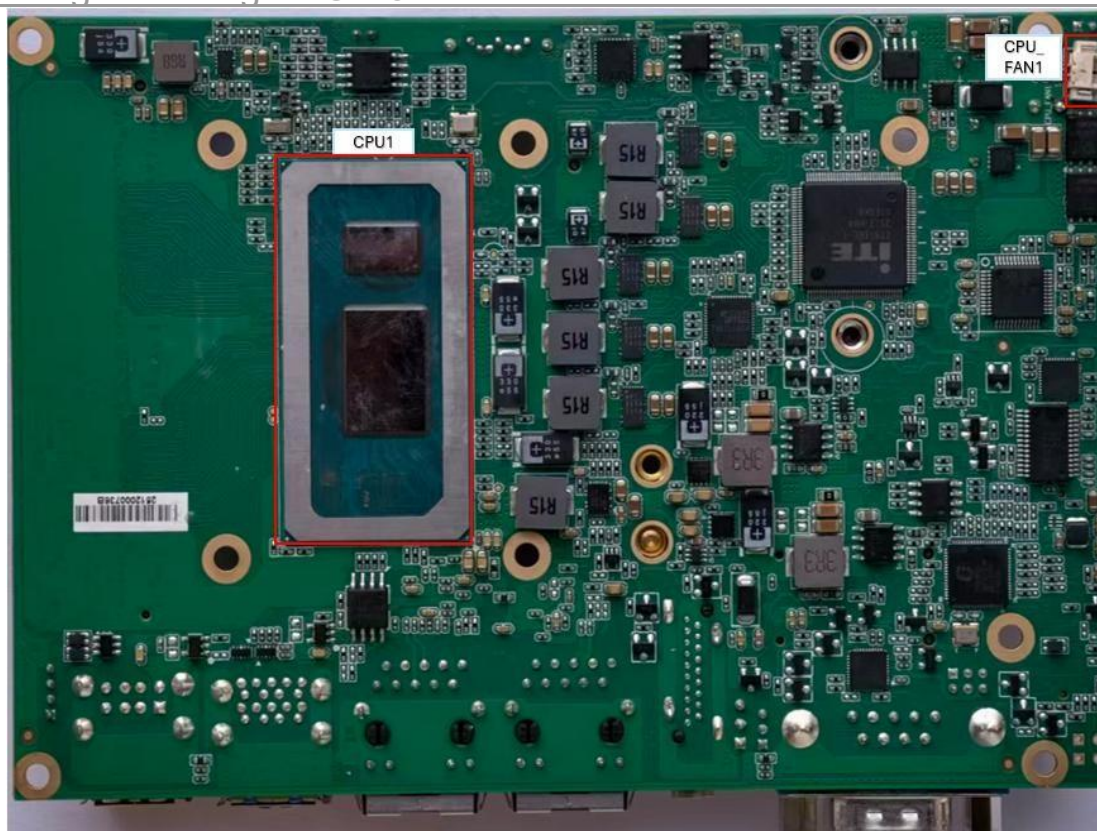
Position der Jumper und Anschlüsse – Unterseite des Mainboards
